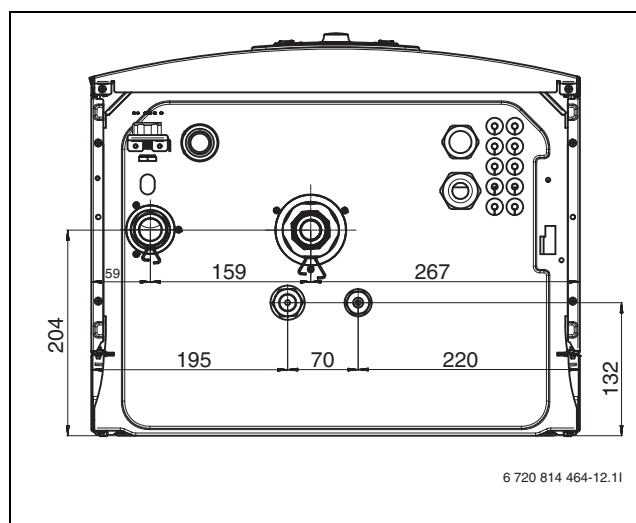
Indeenhed med elektrisk varmelegeme, dimensioner i mm (set nedefra)
